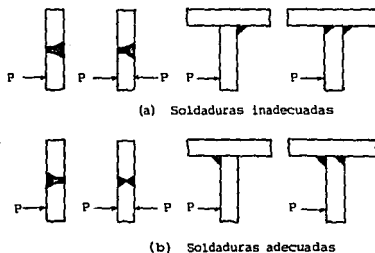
Soldaduras sometidas a flexión.
